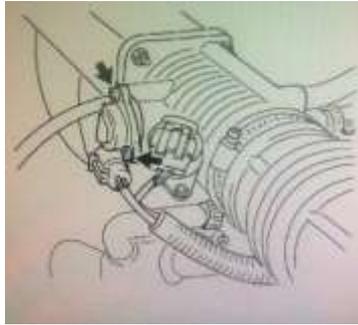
Desconexión de Sockets de Válvula IAC Y Sensor TPS
